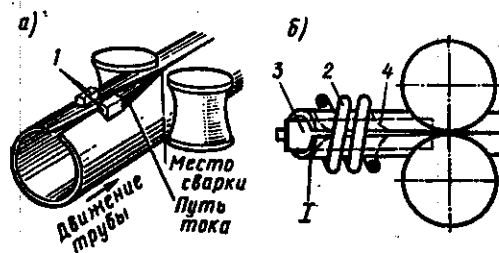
Схема контактной сварки труб токами высокой частоты:
